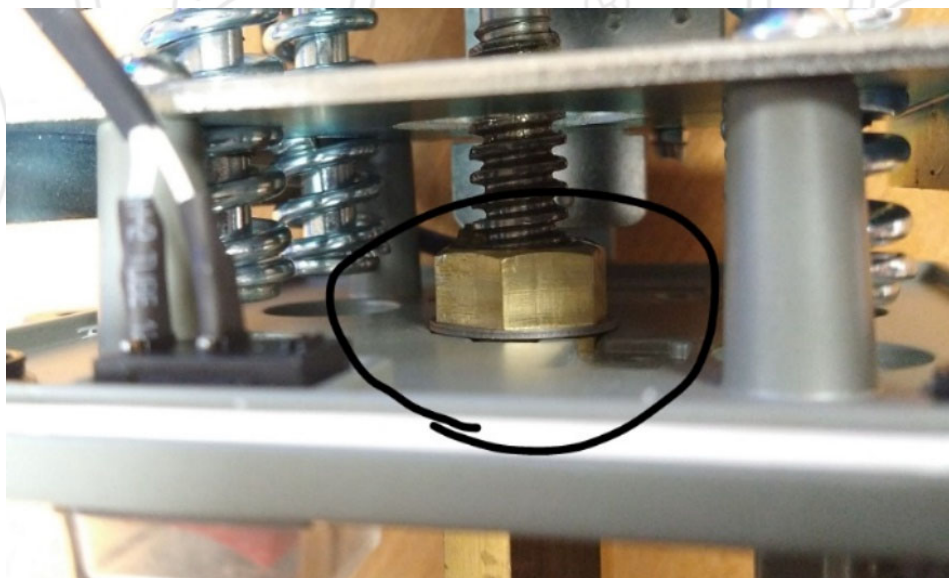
Верхнее стопорное кольцо на штоке привода упирается в корпус – значит плунжер будет закрыт неплотно. Нужно передвинуть плунжер в муфте на 1 виток резьбы ниже.
